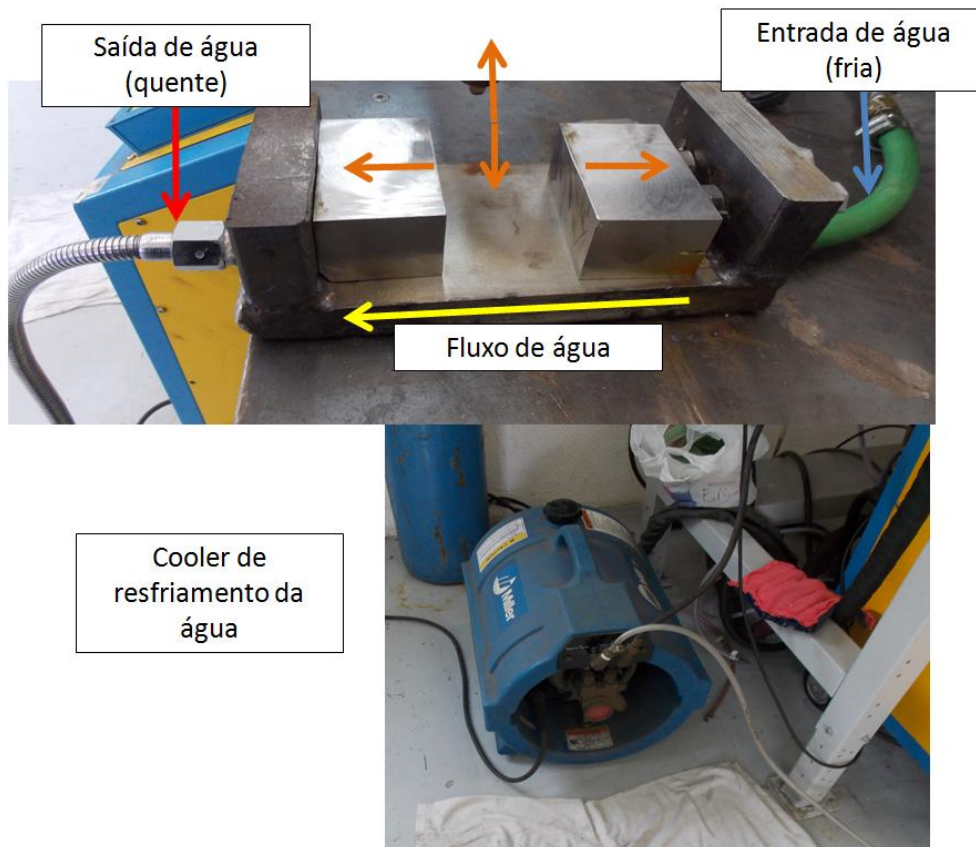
Dispositivo utilizado para resfriar os corpos de prova durante a soldagem
